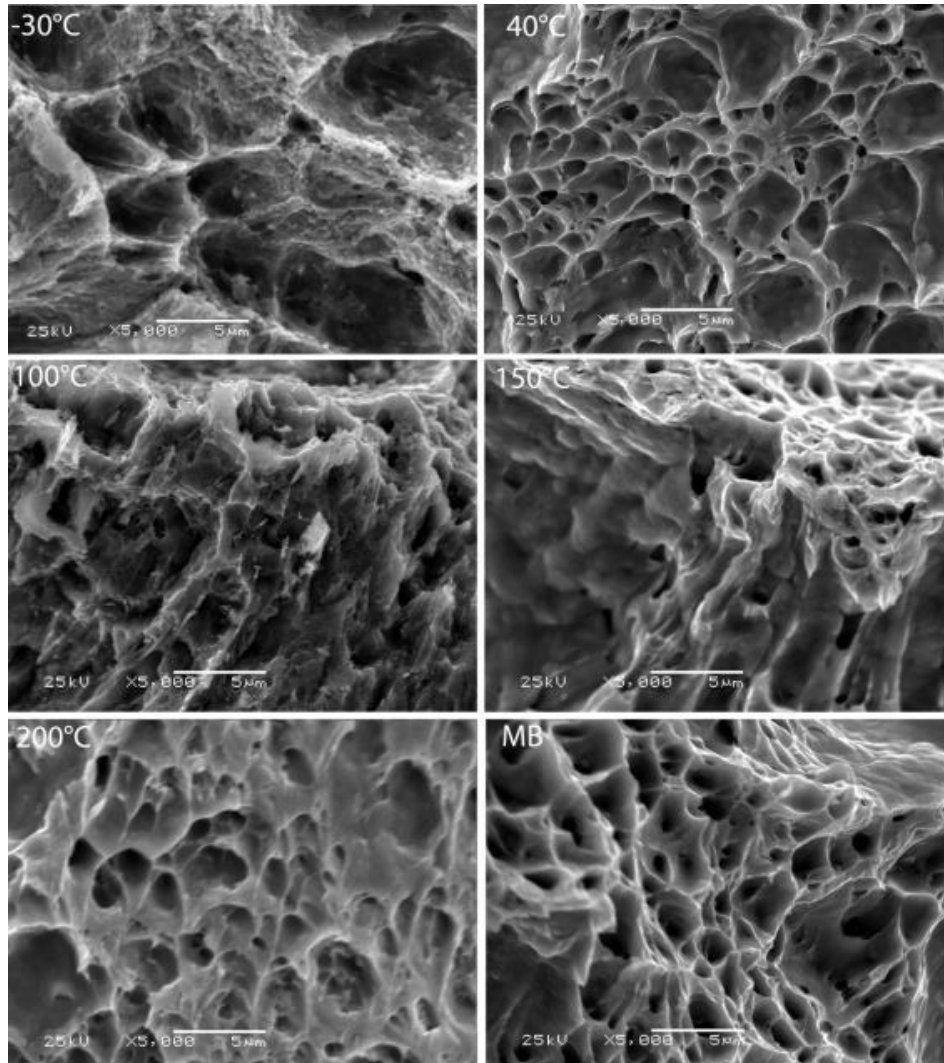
Imagens do MEV das superfícies de fratura das amostras após o ensaio de Impacto Charpy-V realizada a 20 °C. O número posicionado no canto superior esquerdo de cada amostra indica a temperatura de pré-aquecimento da soldagem e MB é metal base.
